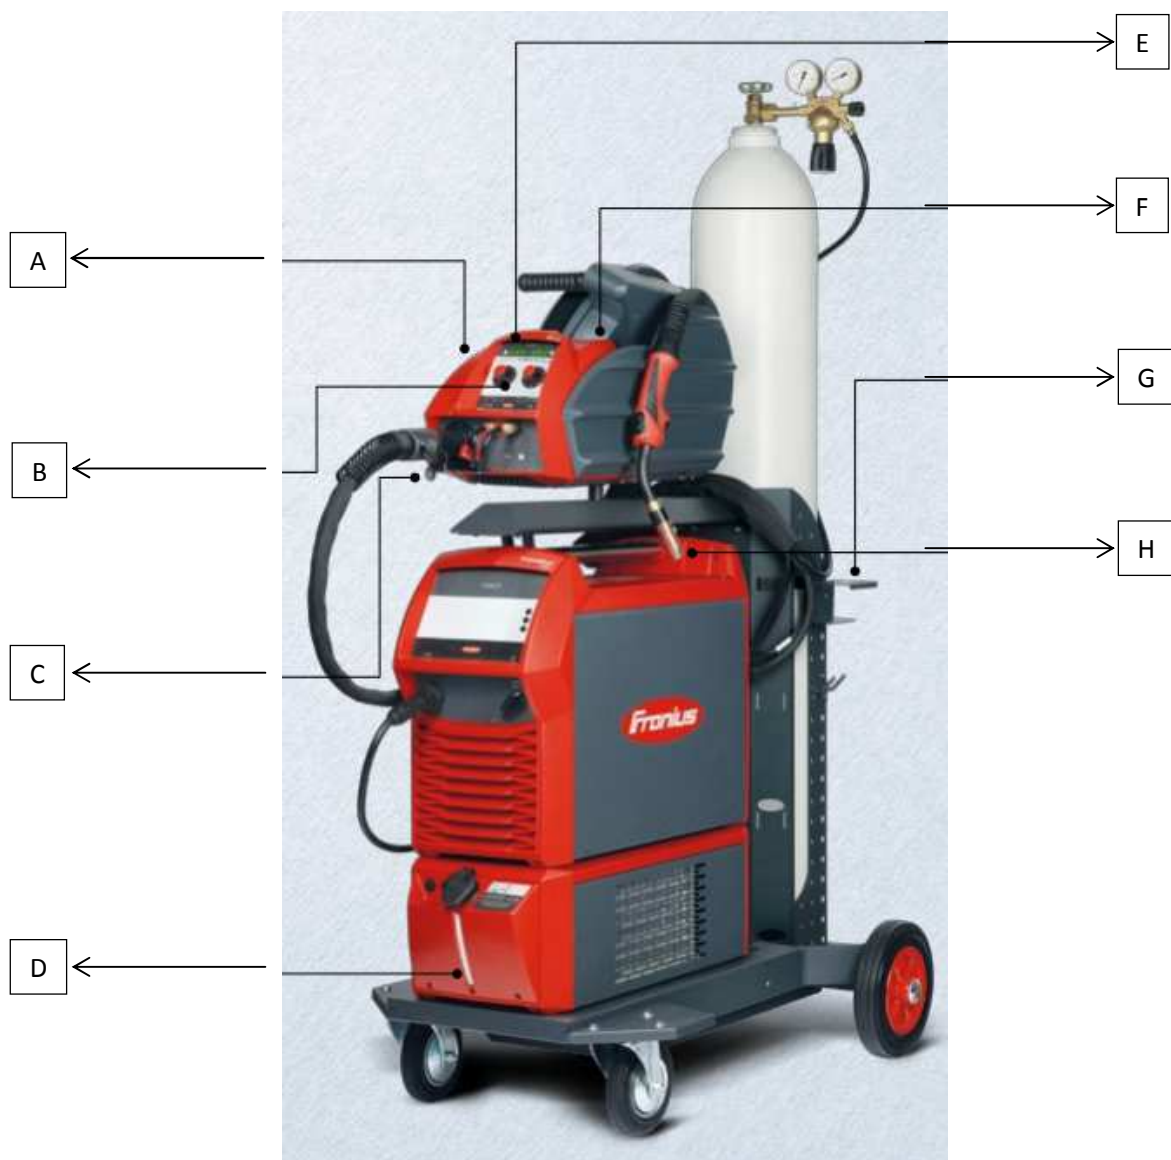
Soldadora FRONIUS Trans Steel 3500/5000 MIG/MAG welding system
